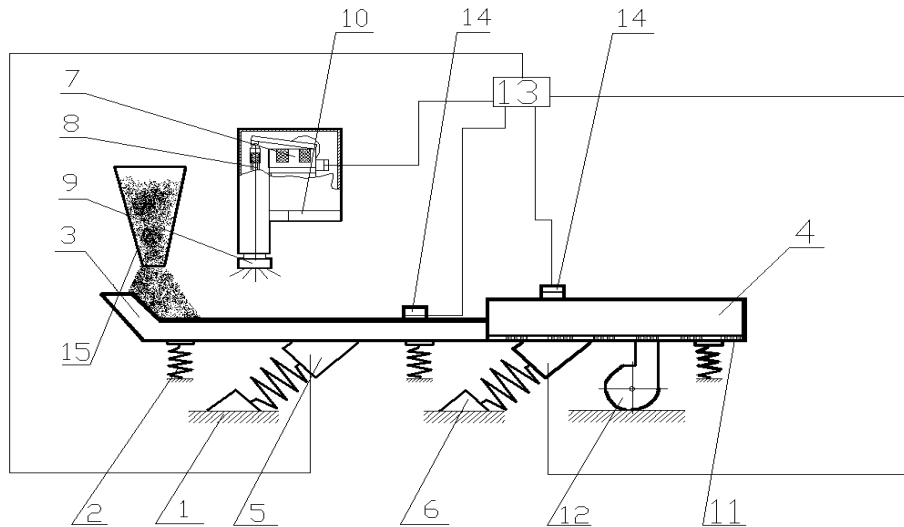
Вибротранспортирующее устройство: 1, 6 – основание; 2 – рессоры лотка; 3, 4 – секции лотка; 5 – вибропривод; 7 – электромагнитный вибропривод распыляющего устройства; 8 – плунжер; 9 – центробежной насос; 10 – корпус распылителя; 11 – перфорированное днище; 12 – сушильная установка; 13 – система управления; 14 – датчики; 15 – обрабатываемый материал
